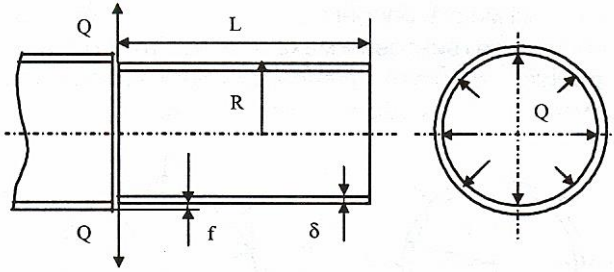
Розрахункова схема вигину кромки обичайки внутрішнім центратором
